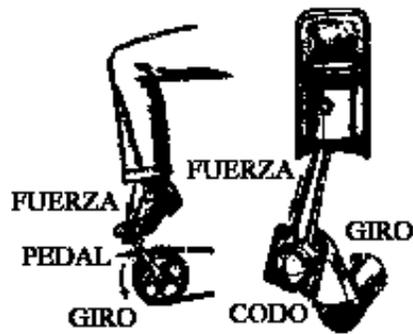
Transmisión de la fuerza de la explosión al cigüeñal.
